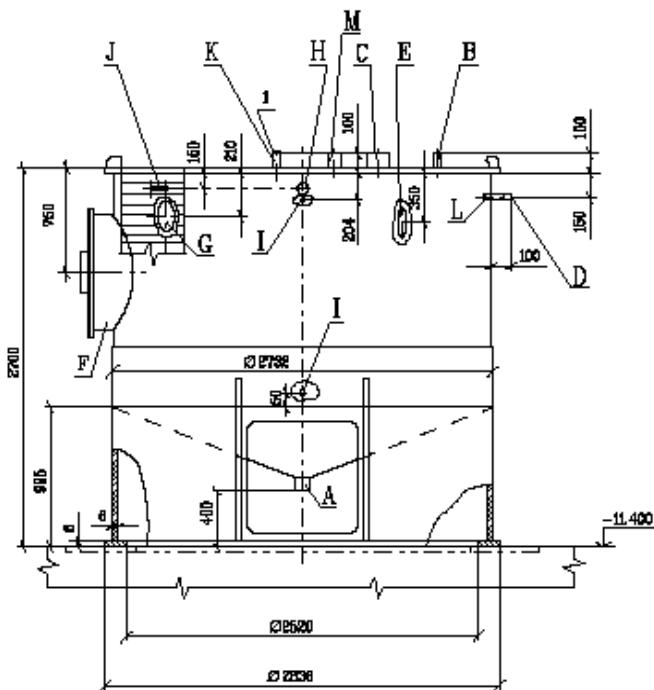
Габаритный чертеж бака боросодержащих дренажей КТС10БВ001
